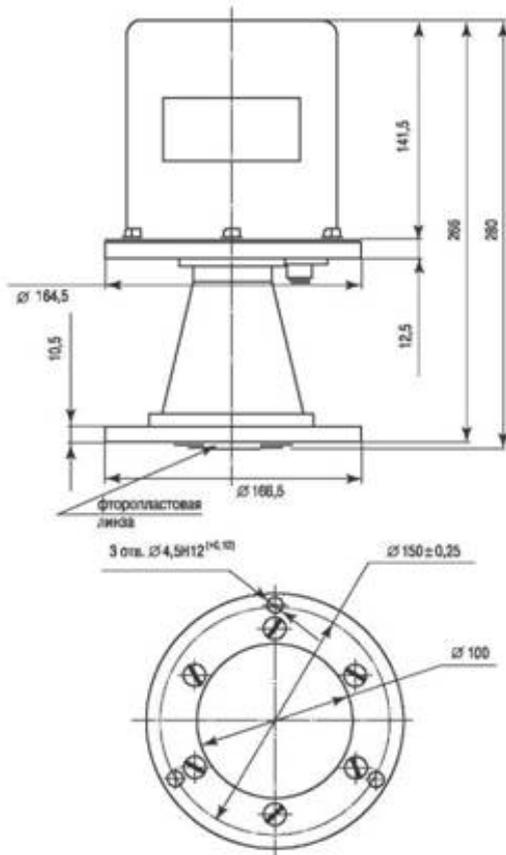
Габаритные, установочные и присоединительные размеры датчика уровня РДУ-Х8, РДУ-Х8И
